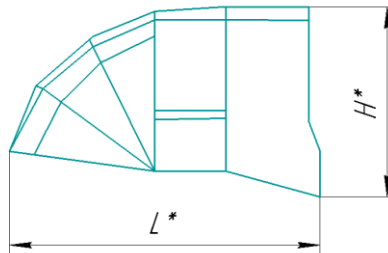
Ковш роторного экскаватора сварного сегментного исполнения (вид сбоку)
